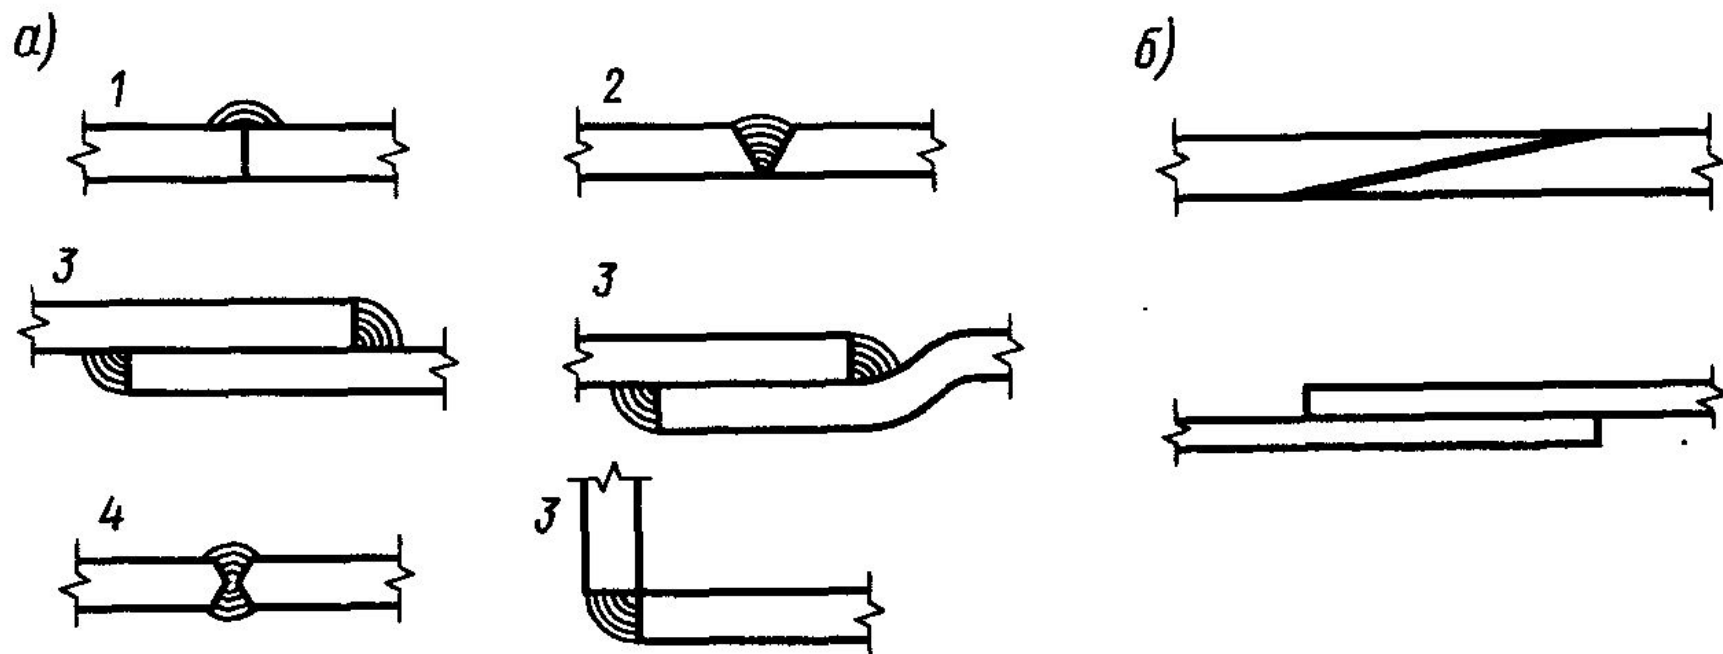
Сварные соединения термопластических пластмасс:
